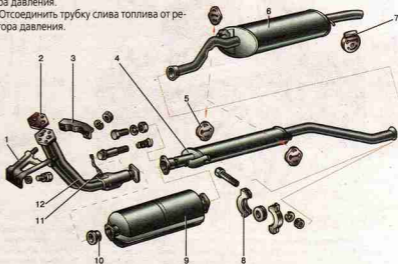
Система выпуска отработавших газов: 1 – кронштейн крепления приемной трубы; 2 – прокладка; 3 – прижим кронштейна; 4 – дополнительный фиксатор; 5 – подшки подвески глушителя; 6 – основной глушитель; 7 – хомут соединения труб глушителей; 8 – нейтрализатор; 9 – уплотнительное кольцо шарнира; 10 – датчик концентрации кислорода; 11 – приемная труба глушителей
